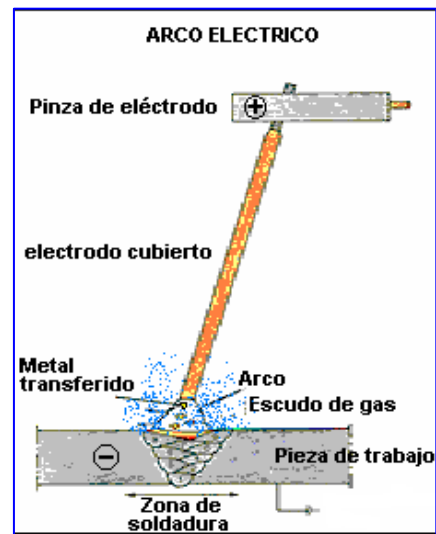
Soldadura arco eléctrico manual recubierto
